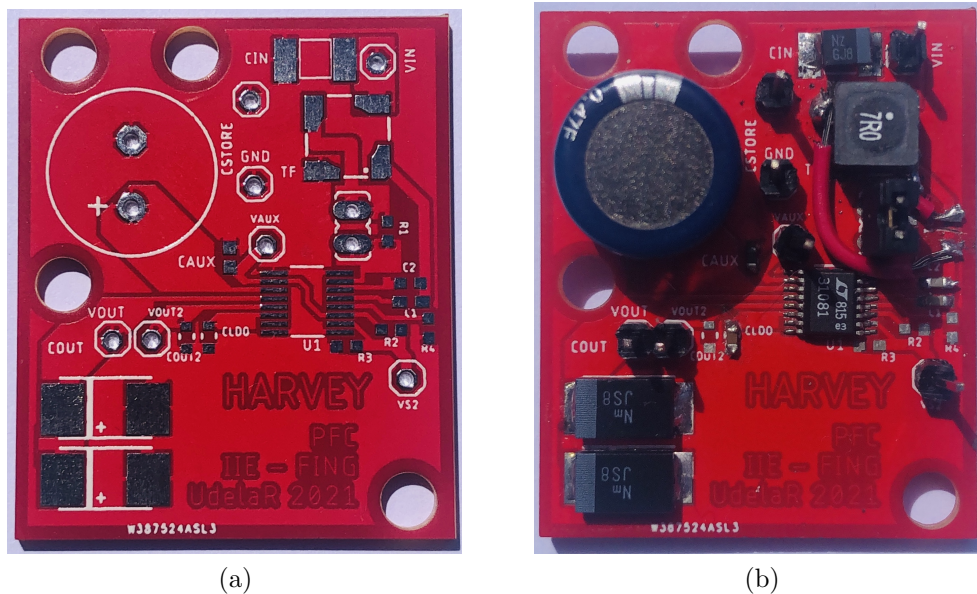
En (a) se presenta el PCB fabricado y en (b) con los componentes soldados y el arreglo de las conexiones del transformador.
